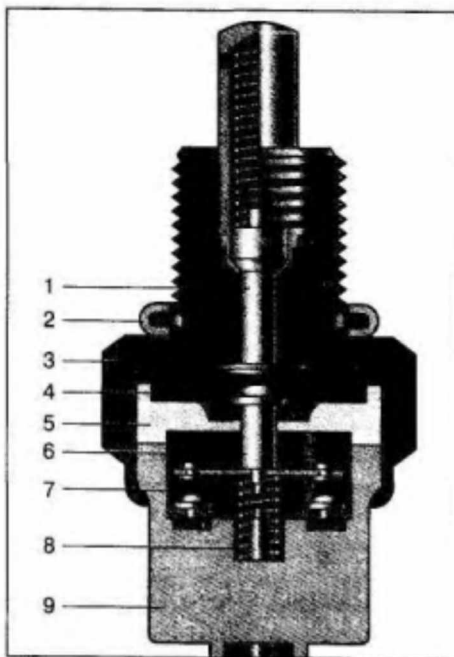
21. Выключатель фонаря света заднего хода 55.3710: 1 — приводной шток (кнопка); 2 — уплотнительное кольцо; 3 — корпус; 4 — мембрана; 5 — вставка; 6 — изолирующий плунжер; 7 — подвижный контакт; 8 — пружина подвижного контакта; 9 — основание выключателя
